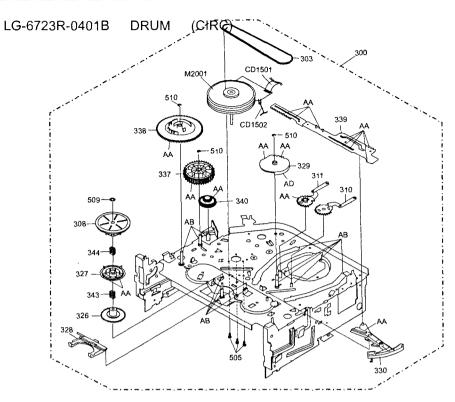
Сборочный чертеж нижней части ЛПМ производства фирмы ORION
